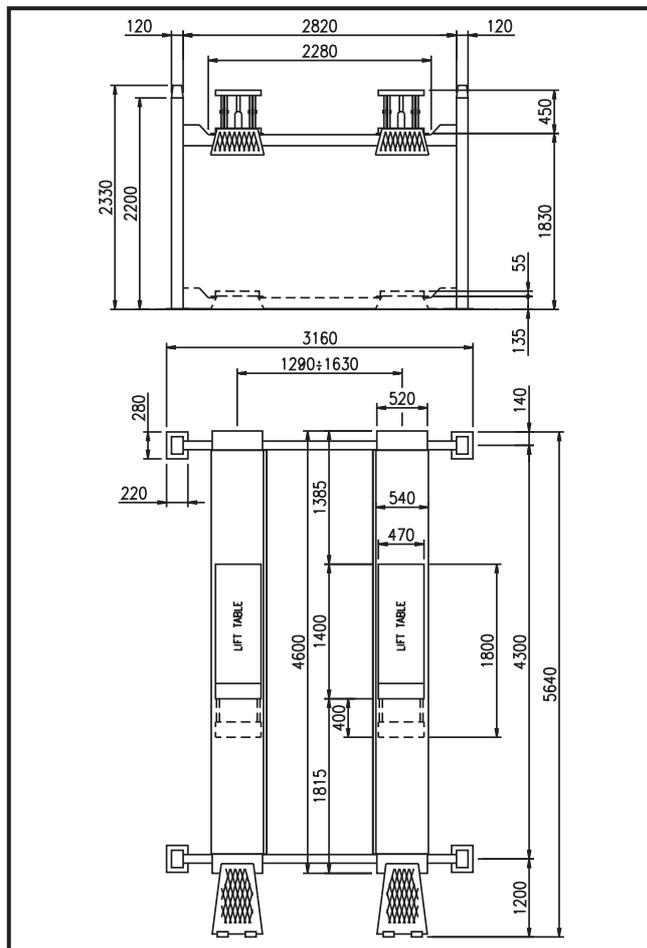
Dimensioni ed ingombri senza kit assetto ruote
